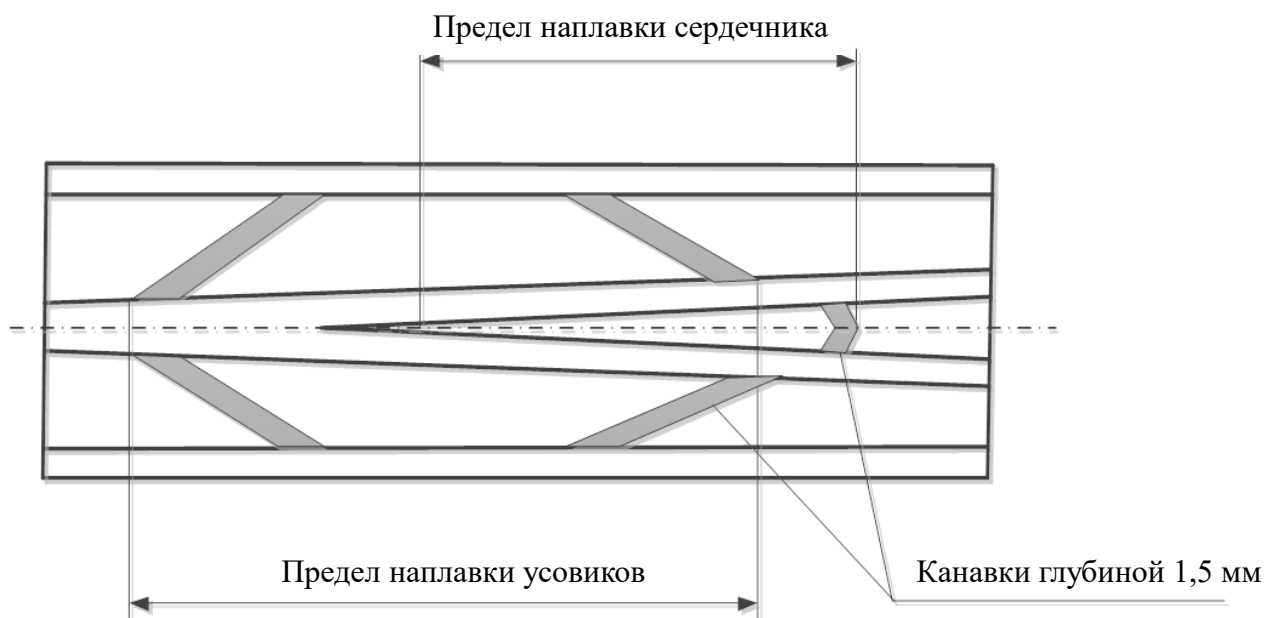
Схема подготовки крестовины к наплавки
